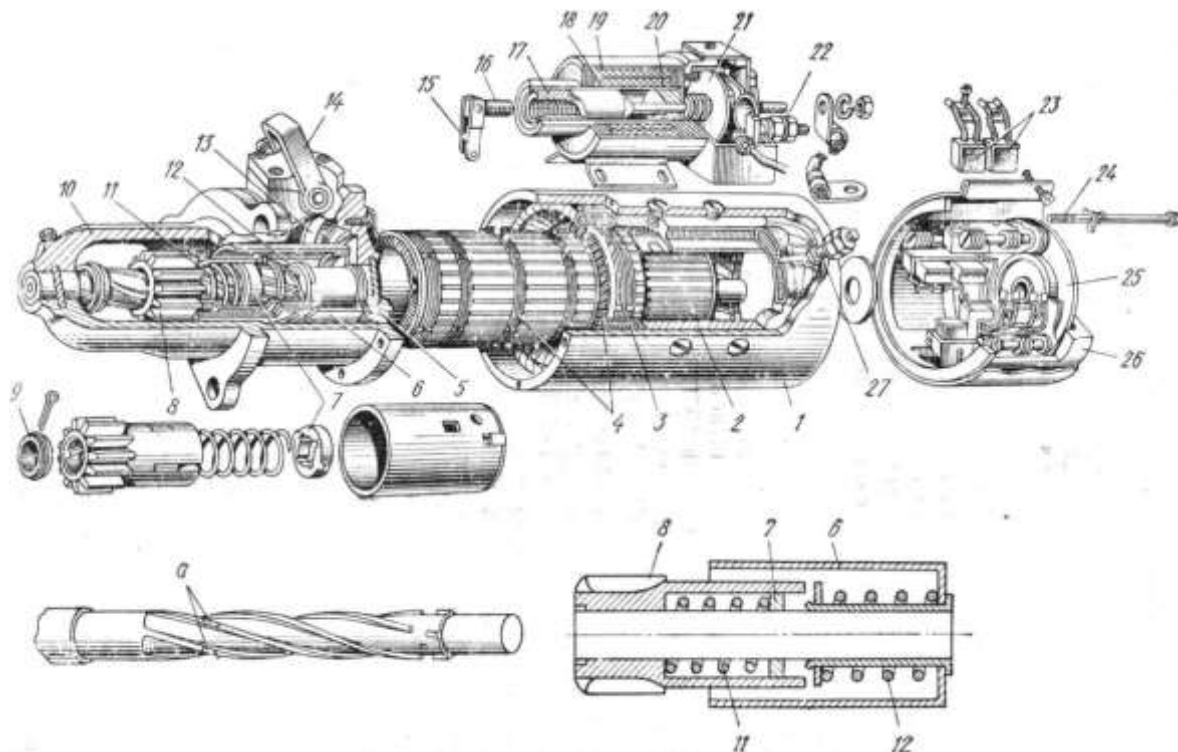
Стартер СТ100: 1-корпус, 2 — полюсный башмак, 3 — катушка, 4 — бандажи, 5 — опорный диск, 6 — стакан 7 — ведущая гайка, 8 — приводная шестерня, 9 — упорное кольцо со шплинтом. 10 — корпус приводного механизма, 11-пружина гайки. 12 — пружина стакана, 13 — внутренний рычаг, 14 — наружный рычаг. 15 — соединительное звено, 16 — регулировочный винт, 17 — якорь реле. 18 — втягивающая обмотка, 19 — удерживающая обмотка. 20 — сердечник, 21 — подвижный контакт. 22 — главный зажим. 23 — щетки. 24 — болт, 25 — траверса, 26 — крышка. 27 — зажим корпуса.
